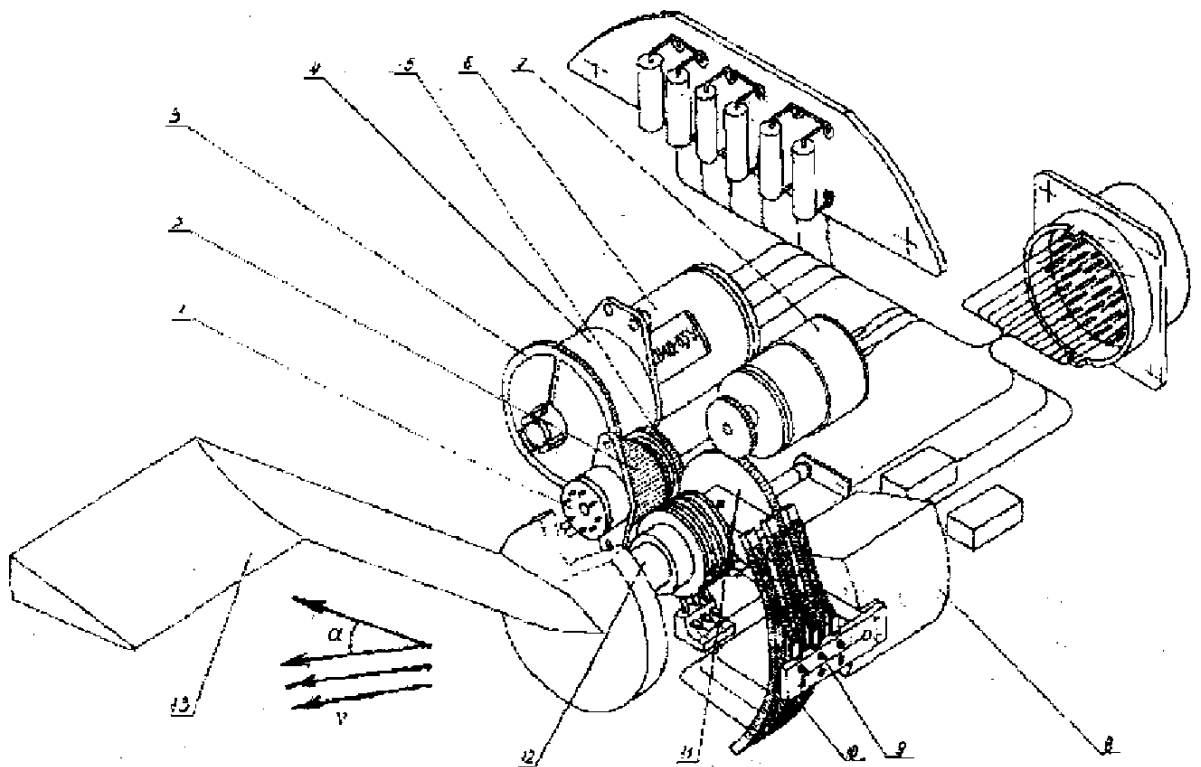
Кінематична схема ДАУ-Ф: 1 - електромагніт; 2 - фрикційна муфта; 3 - шестерня; 4 - редуктор; 5 - шестерня муфти; 6 - двигун; 7 - демпфер; 8 - протывагу; 9 - щіткотримач; 10 - потенціометри; 11 - шестерня на осі флюгера; 12-вісь; 13 - флюгарка
